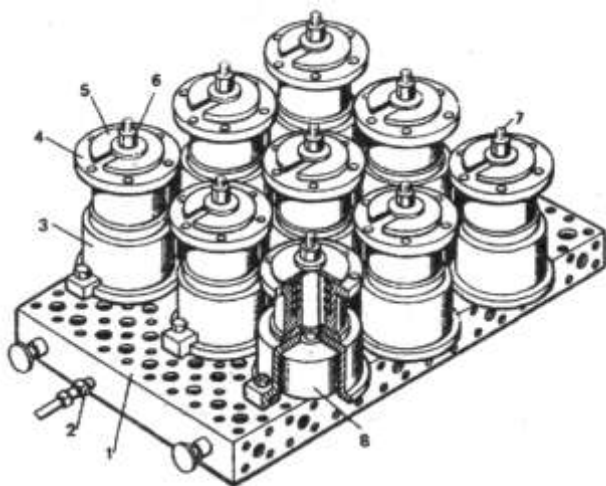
Девятиместное гидравлическое приспособление для установки фланца
